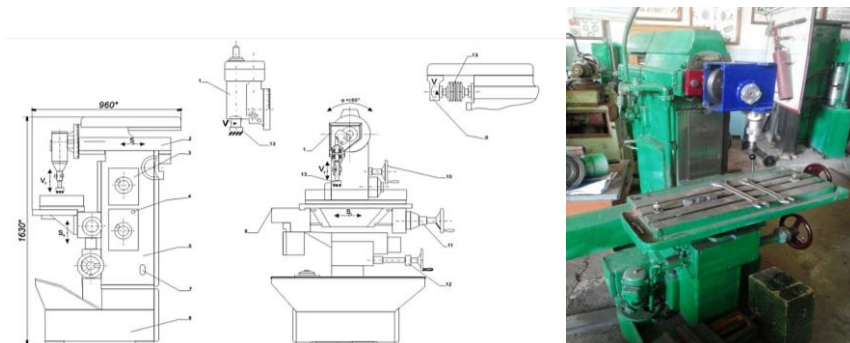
Общий вид виброударного станка для фактурной обработки природного камня.
